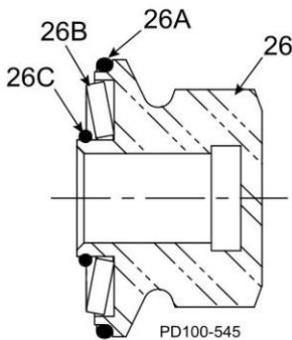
Querschnittsansicht der Montage der Rotornabe, zusammgebaut
